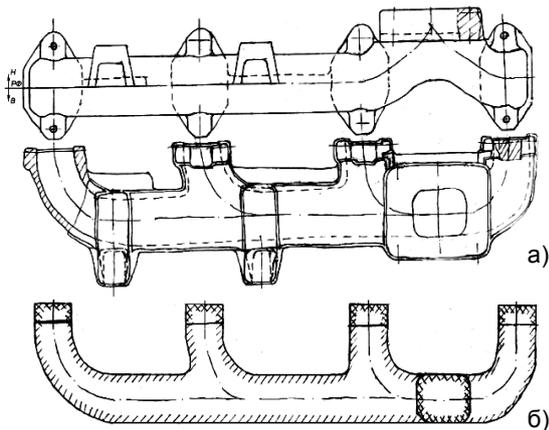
Эскиз отливки “выхлопной коллектор” (а) и эскиз песчаного стержня отливки “выхлопной коллектор” (б)
